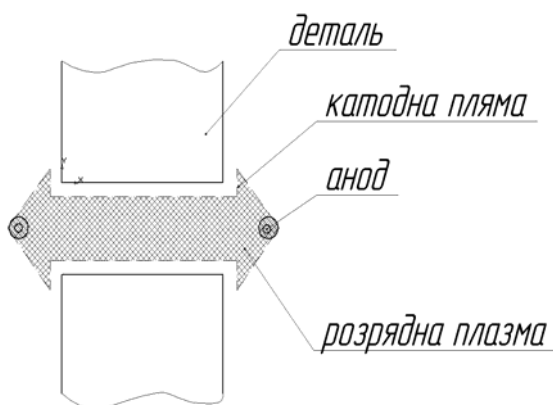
Схема іонної обробки зварюваних поверхонь металів
